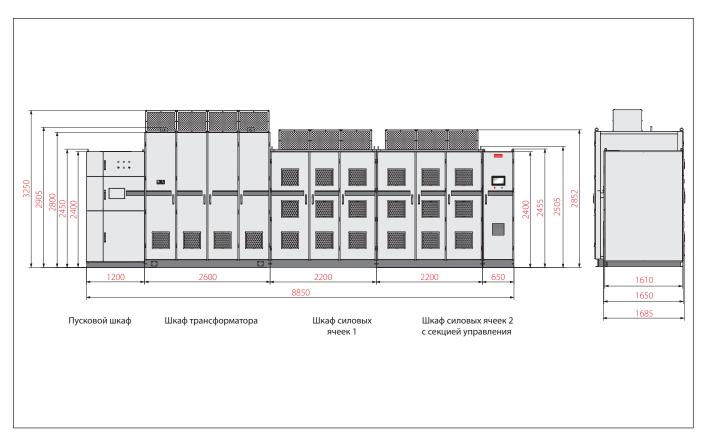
Корпус RAS3 на напряжение 6 кВ
